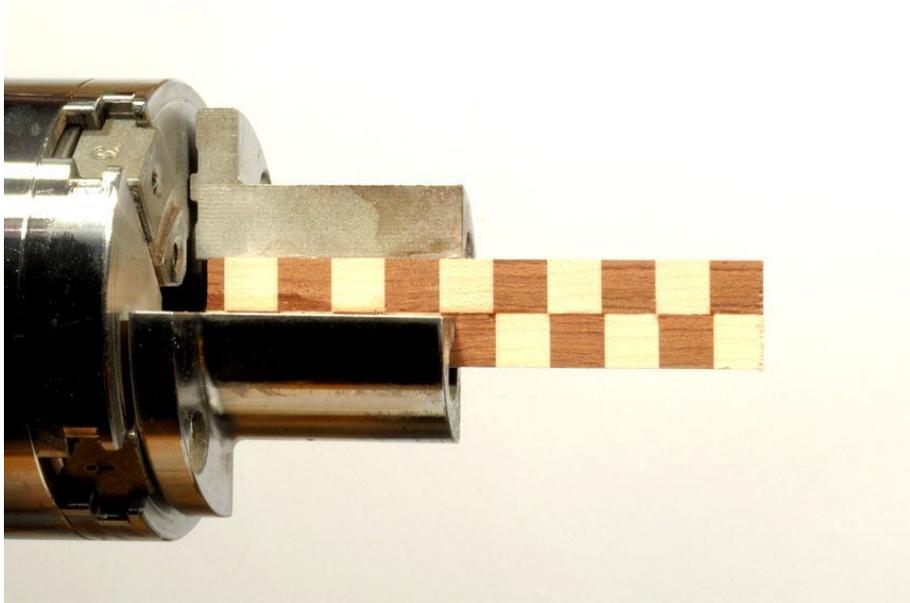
Bohrer einspannen und Bohrtiefe festlegen
